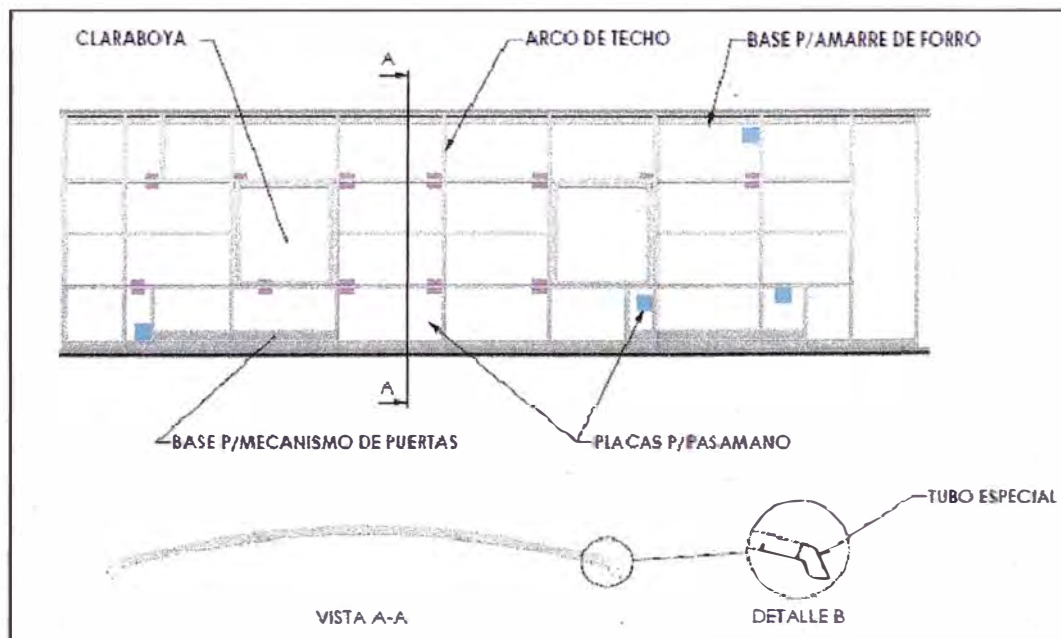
Disposición de los componentes para la estructura del techo.
